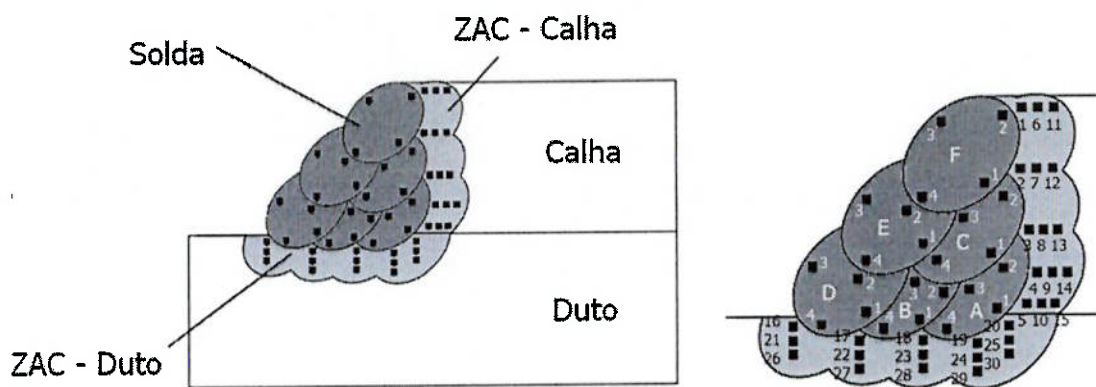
Perfil de varredura da junta soldada por dureza.
